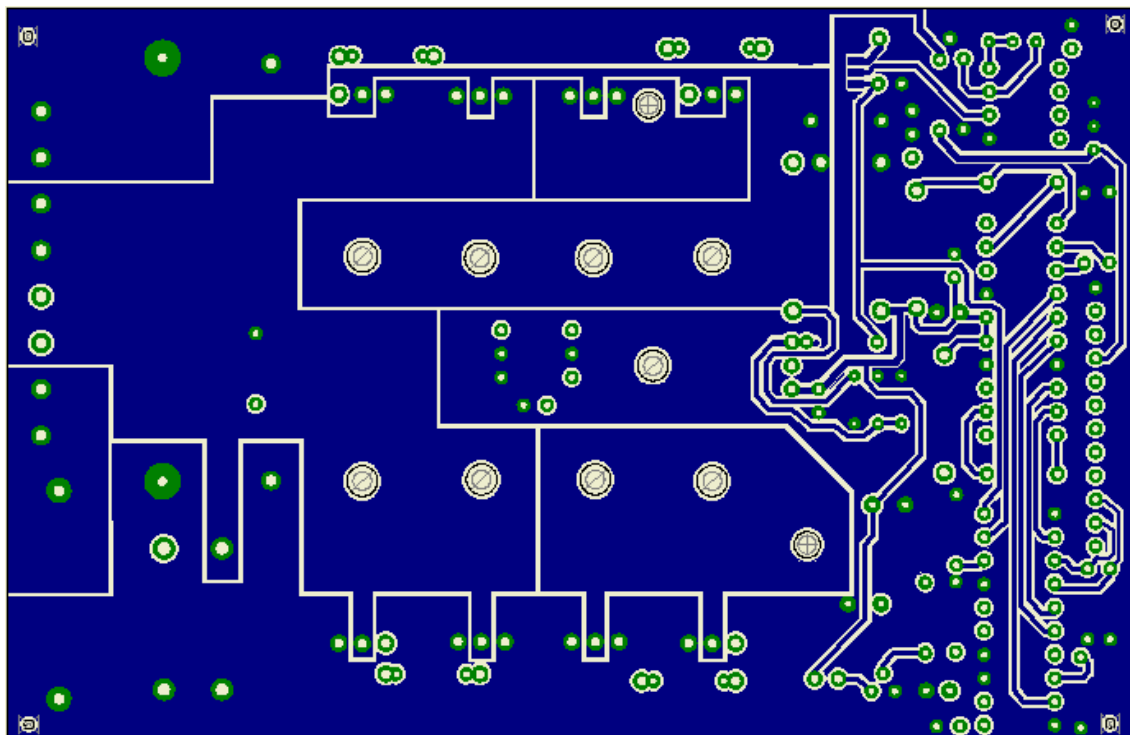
PCB da placa de potência, lado das soldas (bottom)
